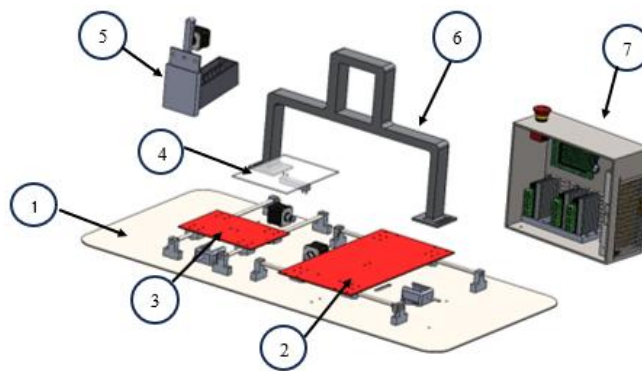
Vista explosionada del ensamblaje de la máquina cortadora y posicionadora de Champiñones.
